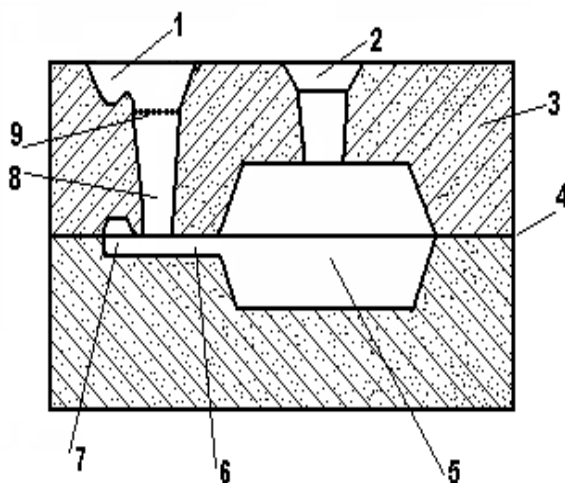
Литниковая система: 1 – литниковая чаша; 2 – выпор; 3 – формовочная смесь; 4 – разъем формы; 5 – рабочая полость; 6 – канал-питатель; 7 – шлакоуловитель; 8 – стояк; 9 – фильтр
